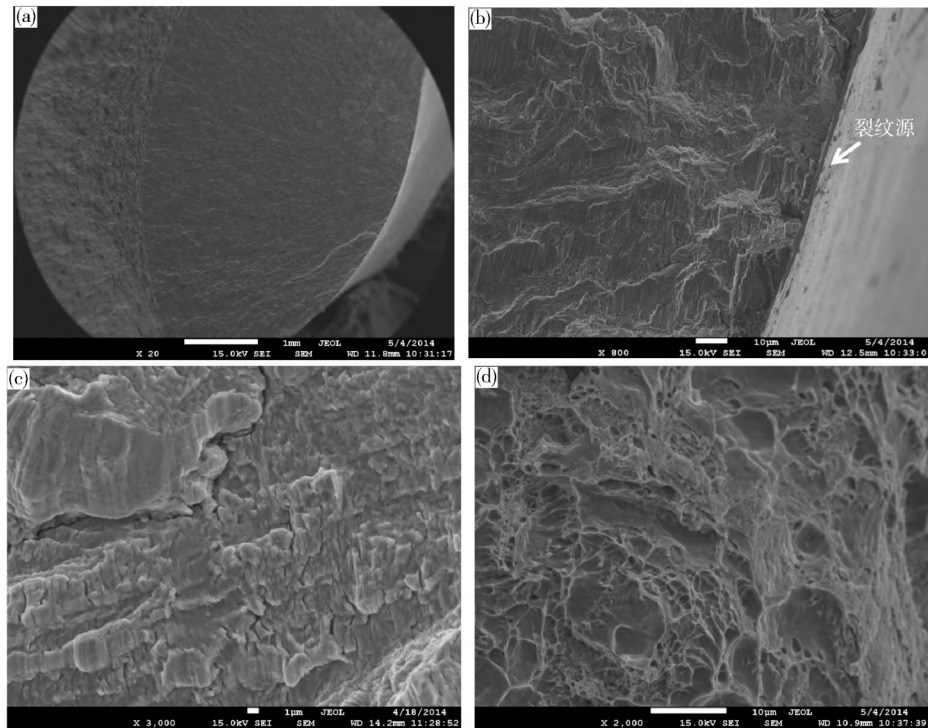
典型光滑试样断口形貌。(a) 断口形貌; (b) 裂纹源; (c) 裂纹扩展区; (d) 瞬断区
